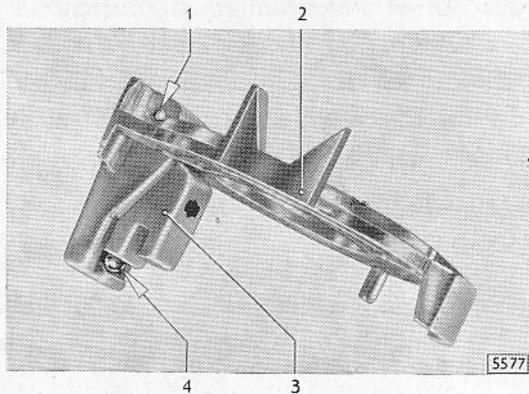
Zusammenbau Gelenkteil mit Lagerstück
